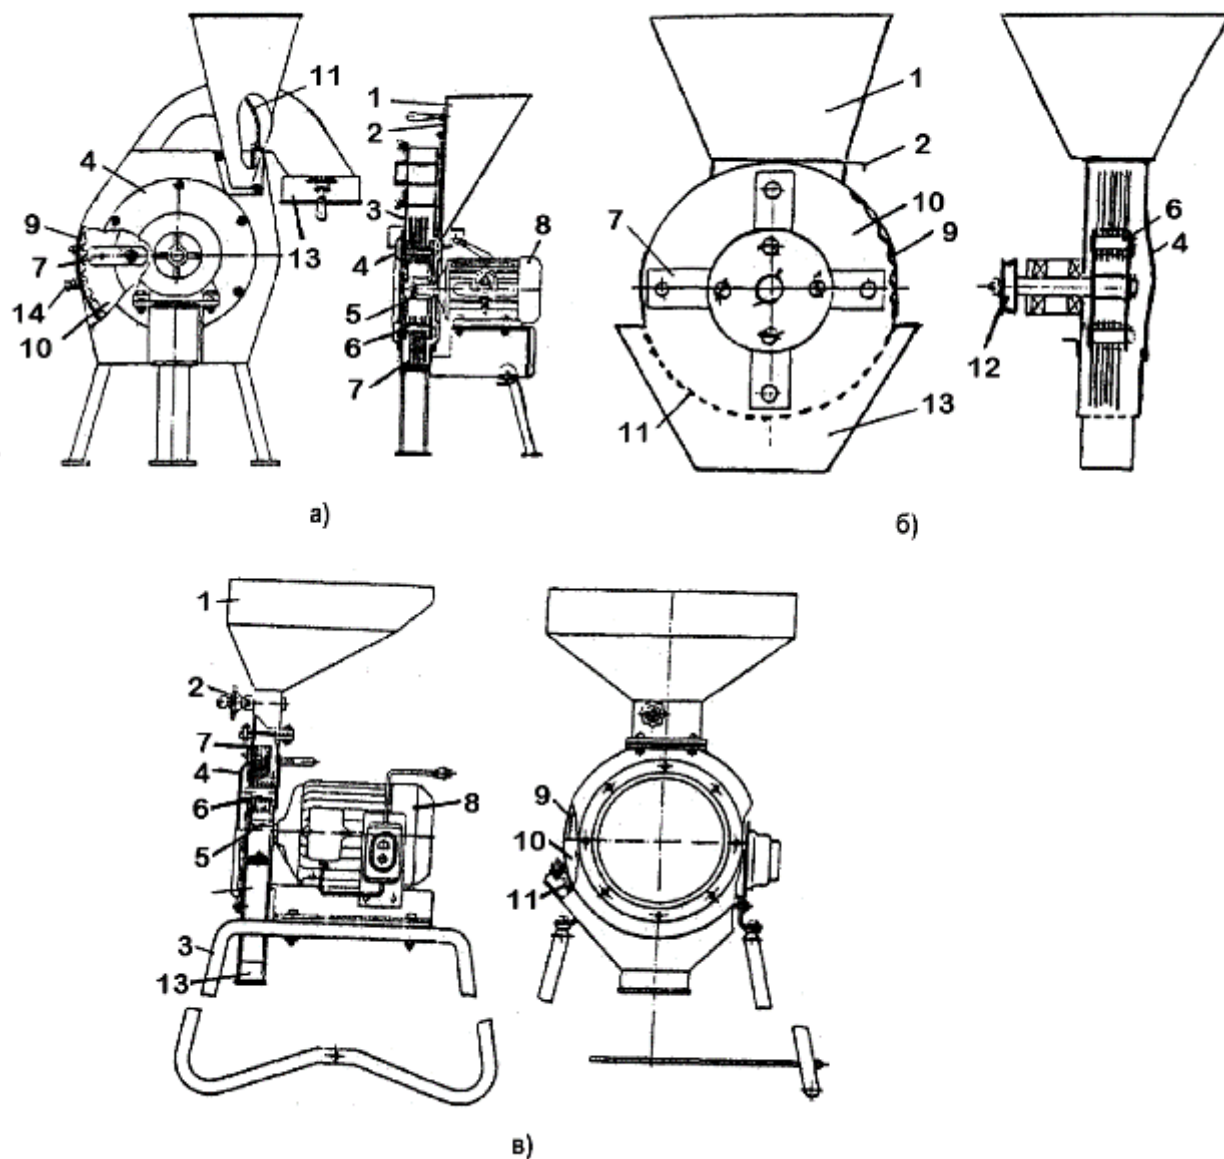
Конструктивні схеми дробарок з шарнірним кріпленням молотків: а) ДЗ-Т-1; б) ИЗ-100; в) "Таврія" 1- завантажувальний бункер; 2- регулювальна засувка; 3- корпус; 4- кришка корпуса; 5- молотковий ротор; 6- вісь; 7- молоток; 8- електродвигун; 9- дека; 10- дробильна камера; 11- решето; 12- вивантажувальний патрубок; 13- вивантажувальна горловина; 14- регулювальний болт
